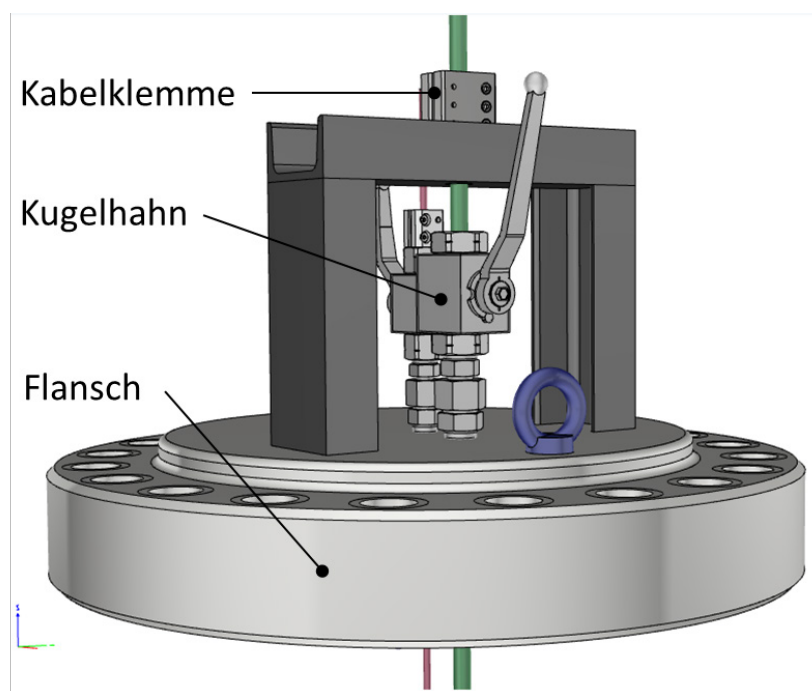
Well Head Flansch mit Kabeldurchführungen
